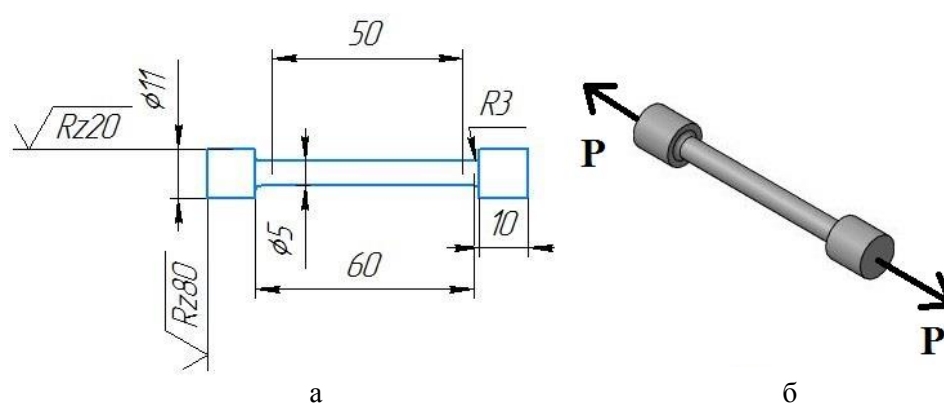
Чертеж образца (а) и схема механического испытания на растяжение (б)
